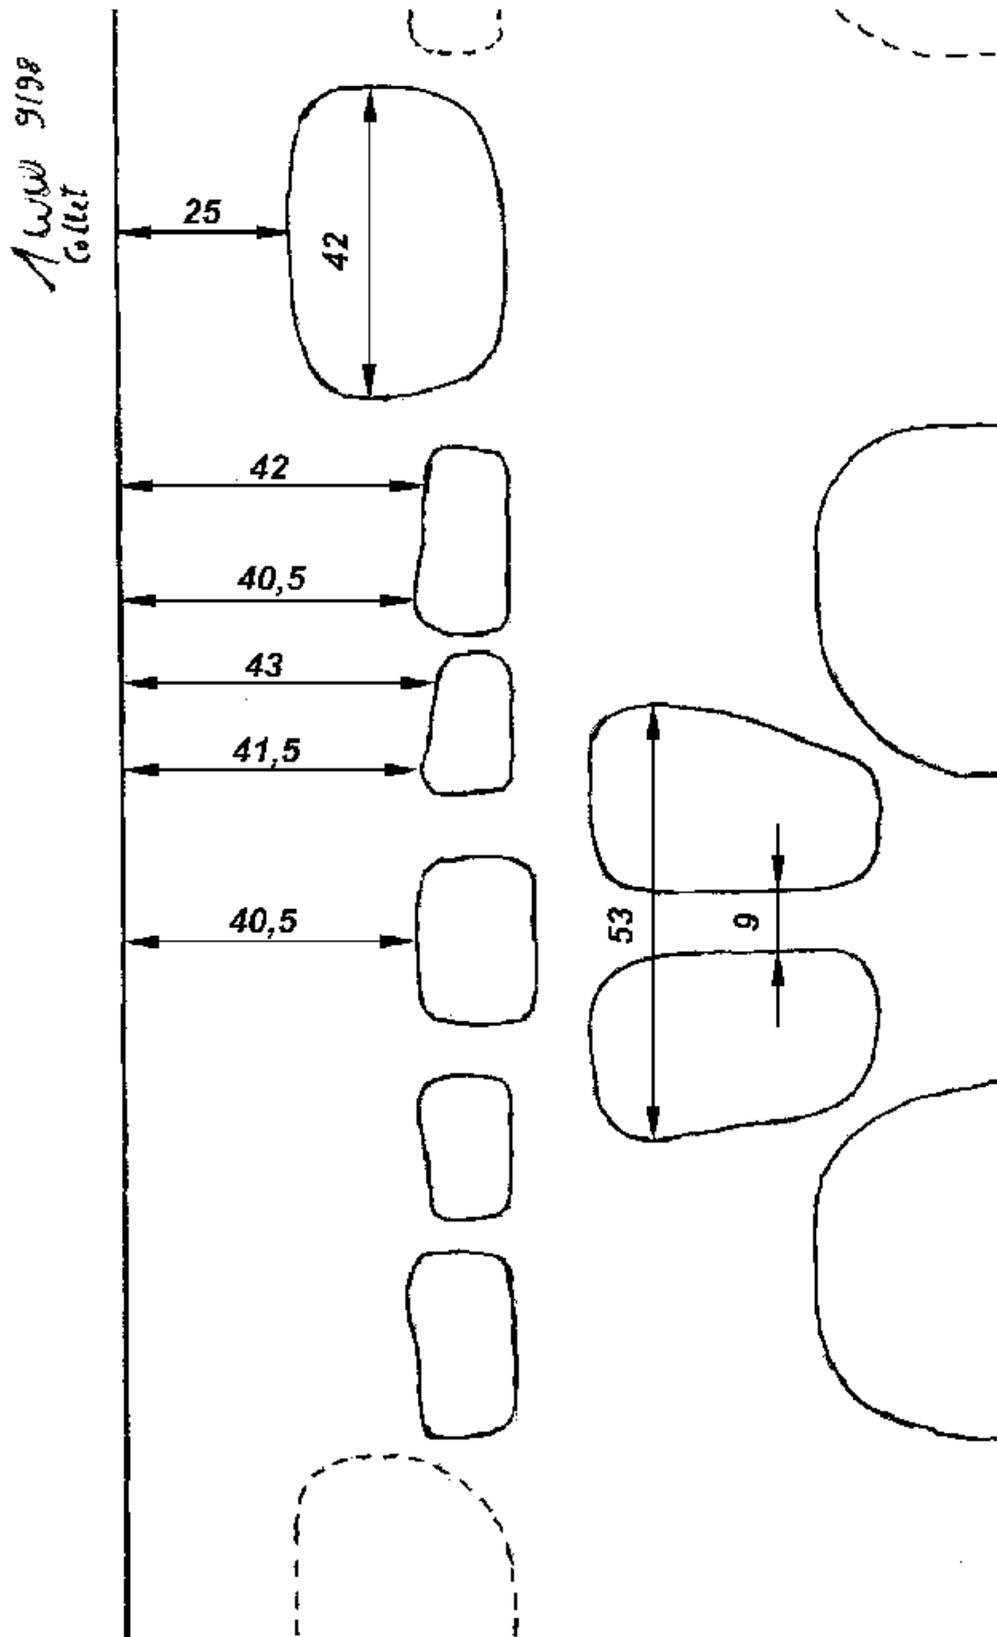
Zylinderabwicklung 1WW / 31K nach der Bearbeitung
